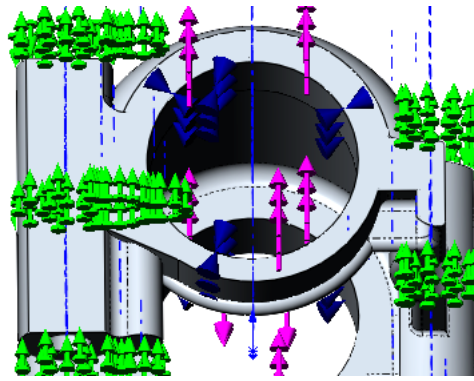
Аналіз підшипника № 4 корпуса
